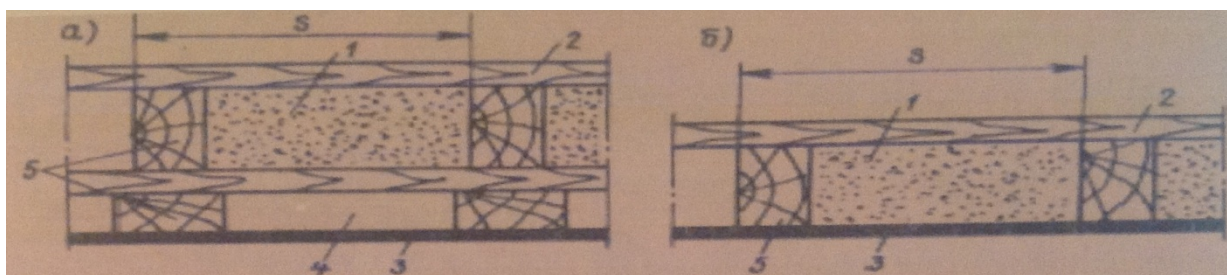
Конструкция изоляции, не прорезаемой судовым набором: а – с воздушной прослойкой; б – без воздушной прослойки
